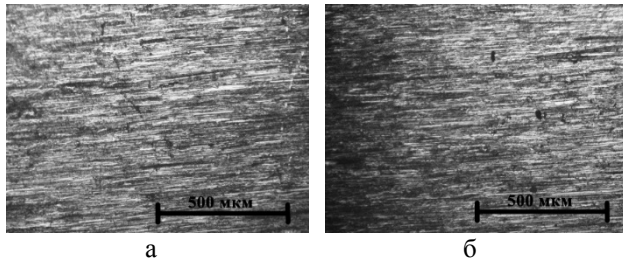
Аэродинамические поверхности пера лопатки после высокоскоростного фрезерования, термической обработки и ручного полирования: а – спинка; б – корыто
